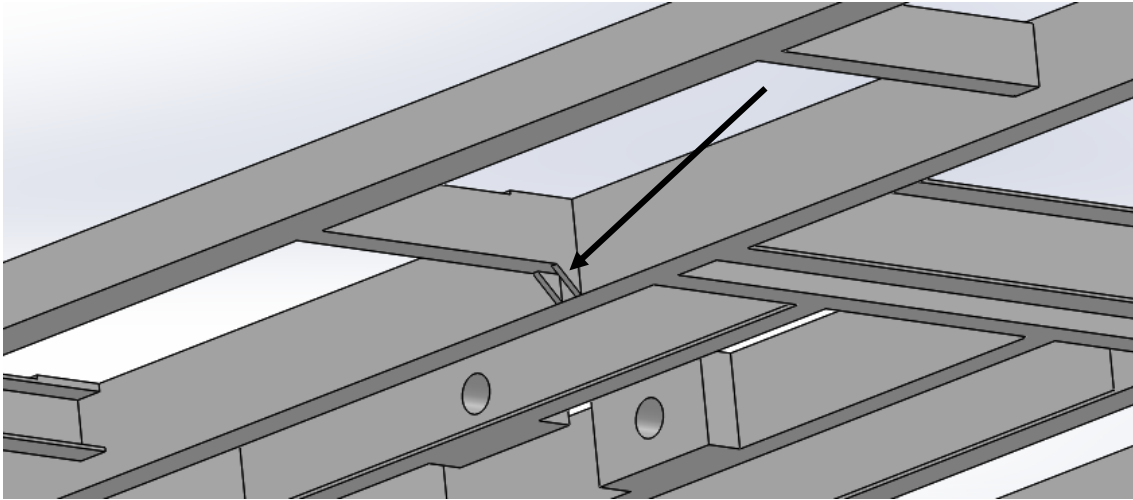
Cuñas de refuerzo en el travesaño exterior.
